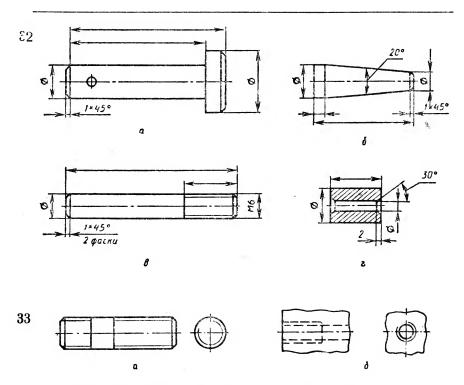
Условные обозначения точеных деталей на чертеже: а — палец; 6 — штифт; в — шпилька; г — втулка.
